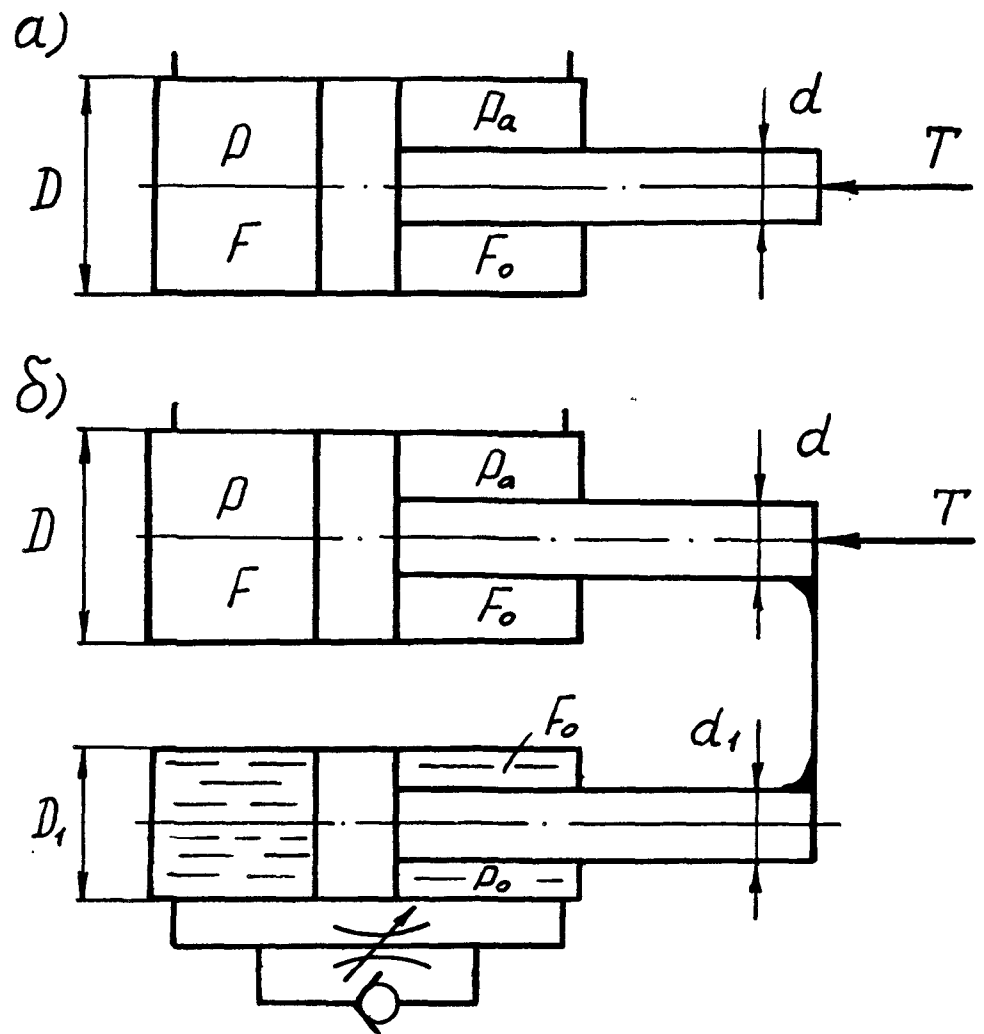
Расчетные схемы: а - пневмоцилиндра двустороннего действия; б - пневмоцилиндра с гидроцилиндром
